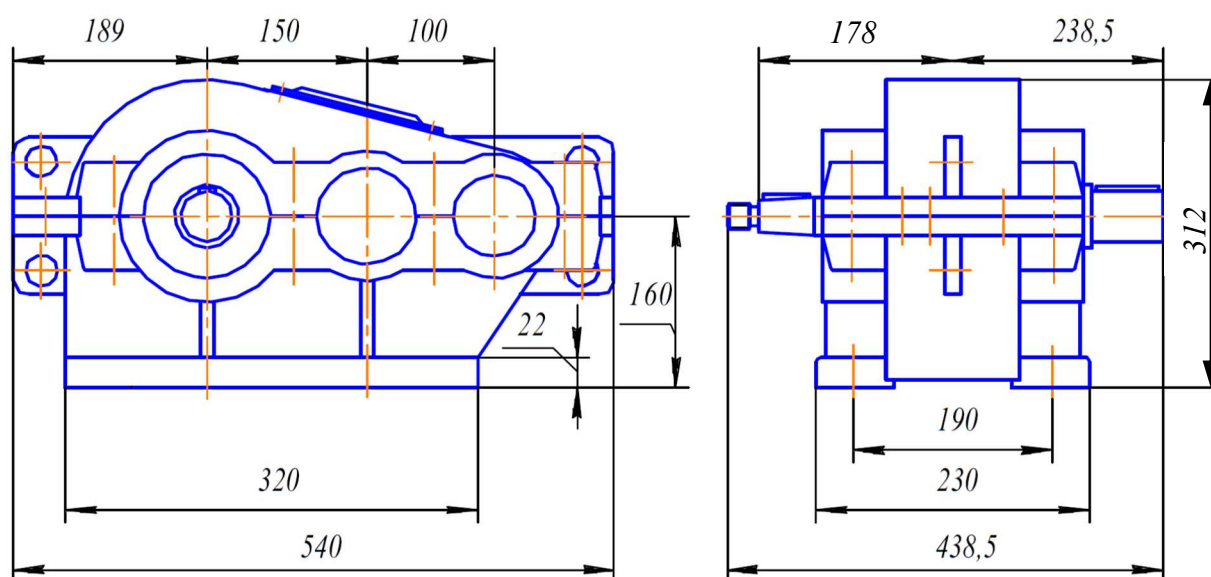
Габаритные и присоединительные размеры цилиндрического редуктора
